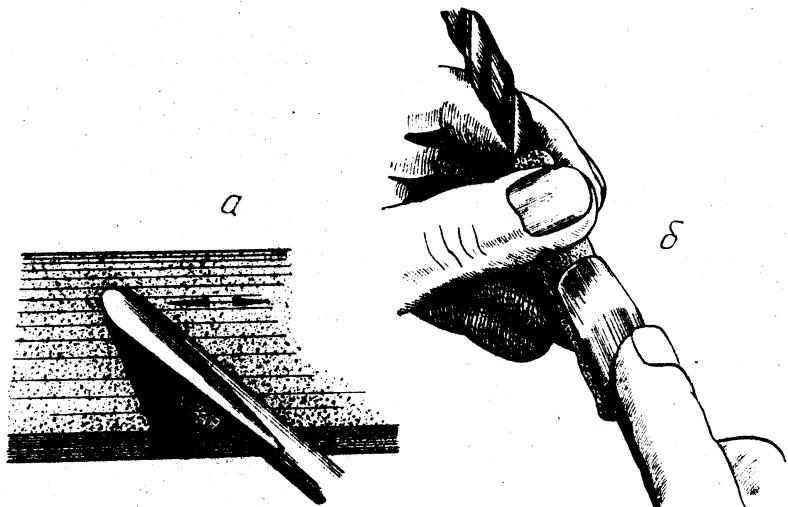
Заточка полукруглых стамесок и резцов: а — направление движения руки при заточке со стороны фаски; б — использование гладкой части сверла и полоски паждачной бумаги для правки стамески со стороны желобка [лица]
